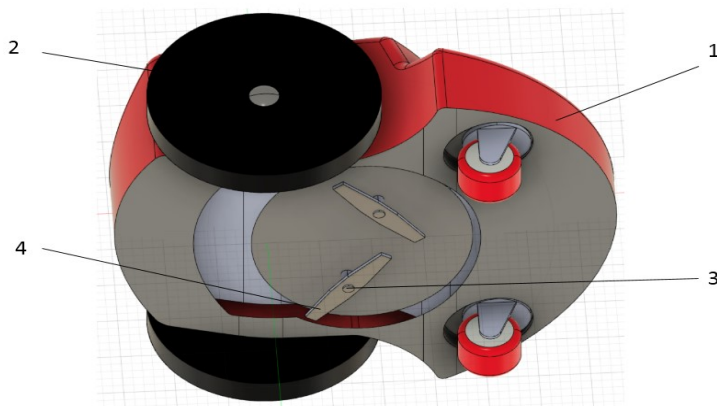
Конструктивная схема робота-газонокосилки (1 – корпус; 2 – колеса; 3 – вращающийся вал; 4 – режущий инструмент (лезвие))
